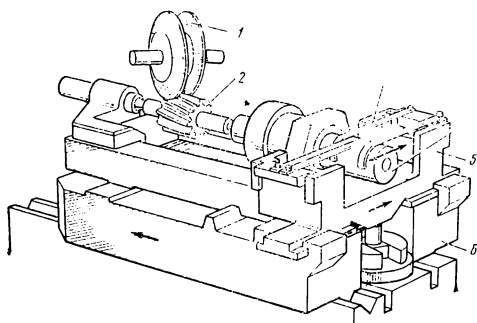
Шлифовальный станок с двумя тарельчатыми шлифовальными кругами
